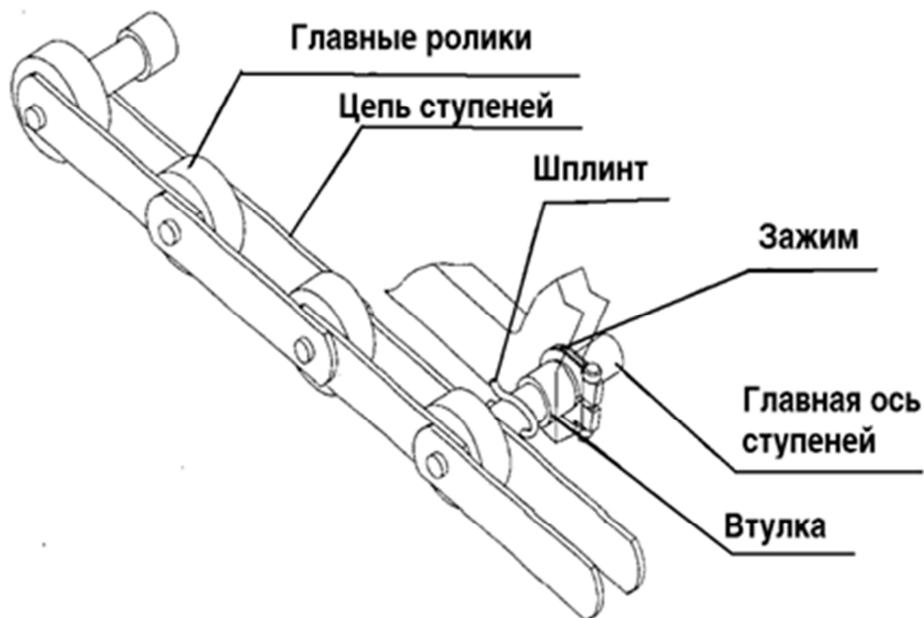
Схема крепления ступени к тяговой цепи
